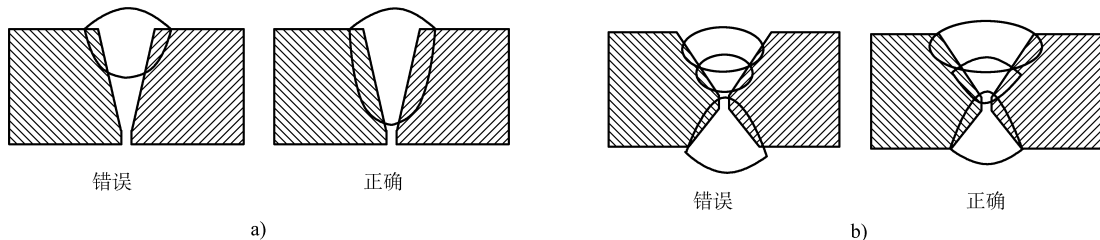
特殊部位焊缝的适宜焊接电压
